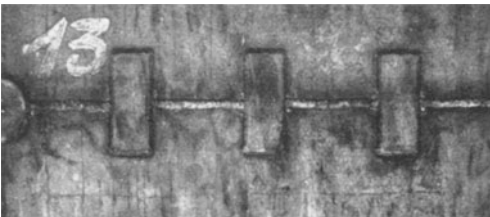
Mit Laschen gesicherte Schweißnaht.
